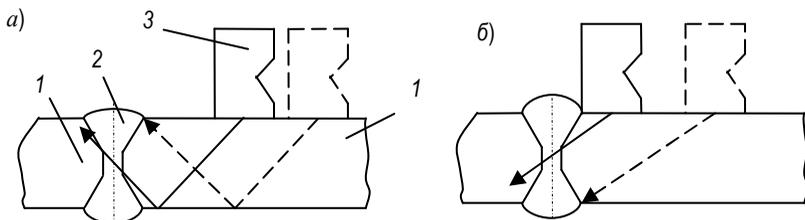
Схемы контроля стыковых сварных соединений:
